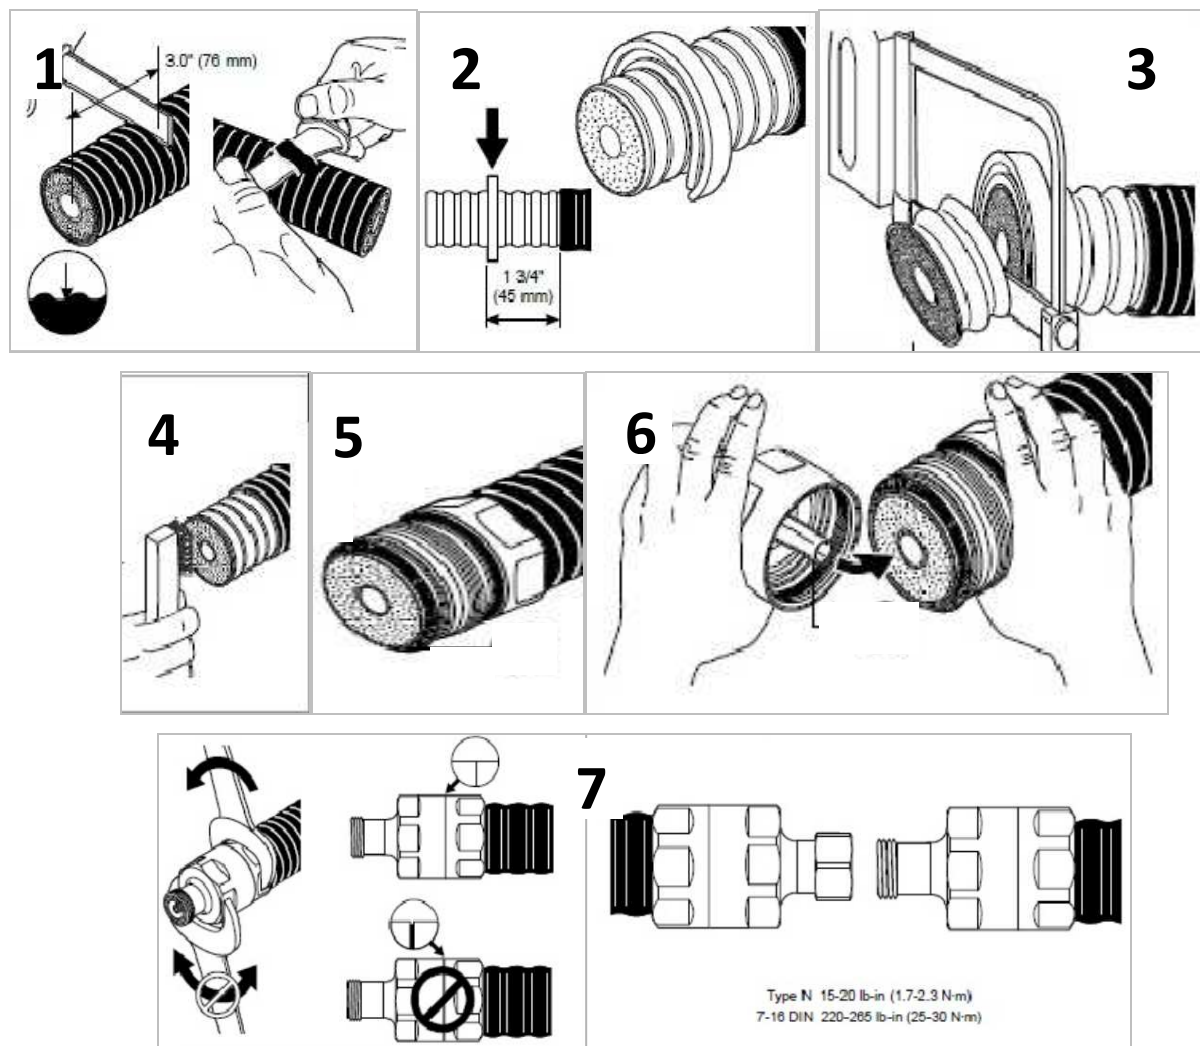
Ensamblaje de un conector en cable coaxial [19].
